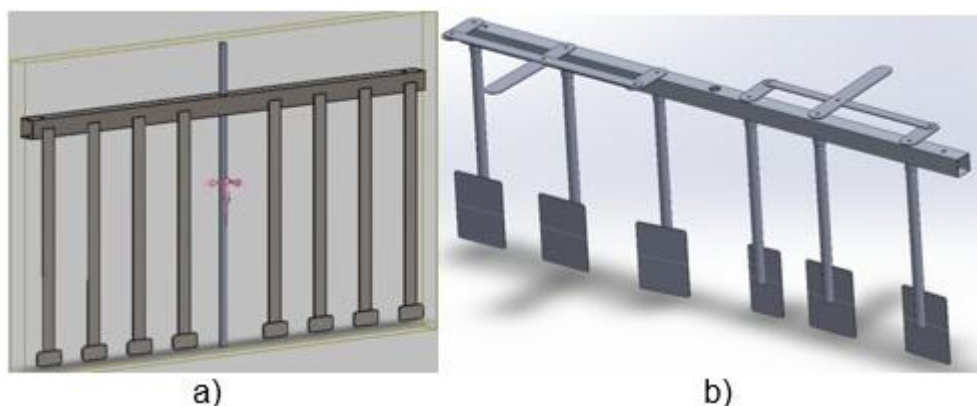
Removedor de paletas, a) diseño anterior y b) rediseño
